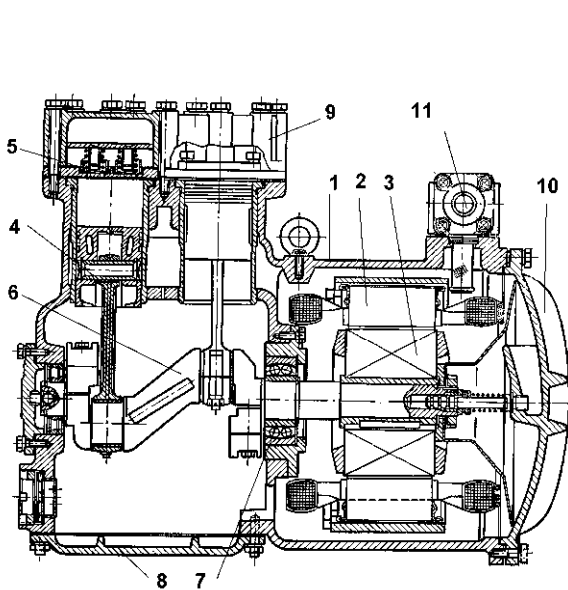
Компресор ФВ6БС (5П7-2-0, 24) безсальниковий, вертикальний, двоциліндровий, непрямоточний, з безпосереднім приводом: 1 - блоккартер; 2 - статор електродвигуна; 3 - ротор електродвигуна; 4 - шатунно-поршнева група; 5 - клапанна група; 6 - колінчастий вал; 7 - корінний підшипник; 8 - нижня кришка; 9 - верхня кришка; 10 - бічна кришка; 11 - всмоктувальний вентиль
